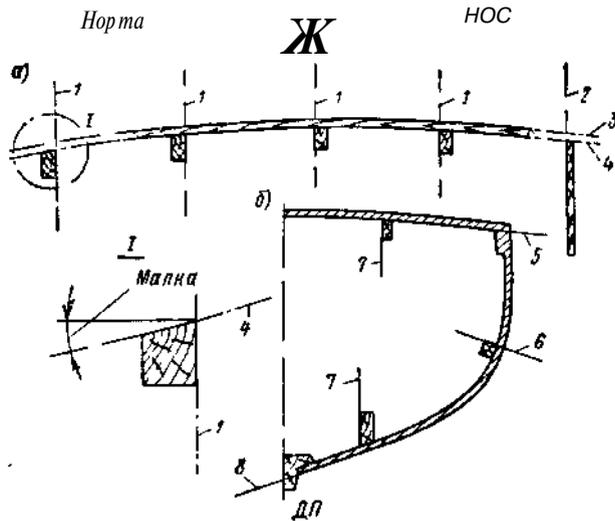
Положение теоретических линий конструктивных элементов корпуса: а — план корпуса; б — поперечное сечение.
